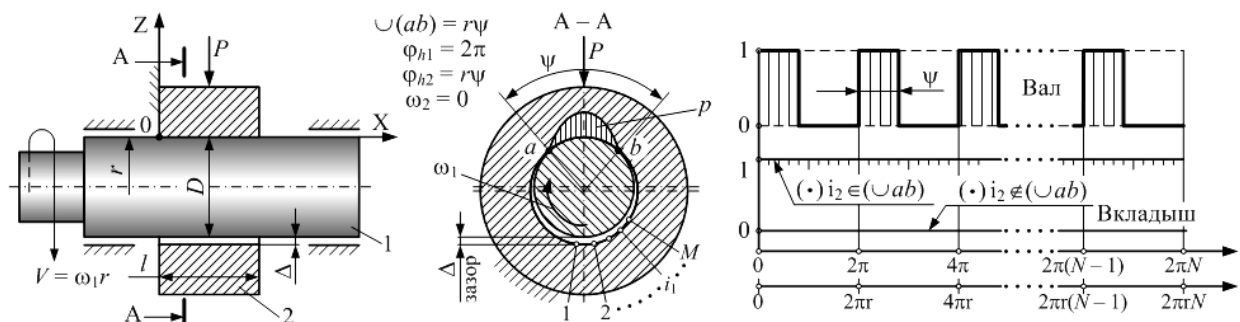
Модель контакта поверхностей вкладыша и вала цилиндрического подшипника трения скольжения
